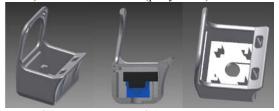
Сборка корпуса в САПР Autodesk Inventor
